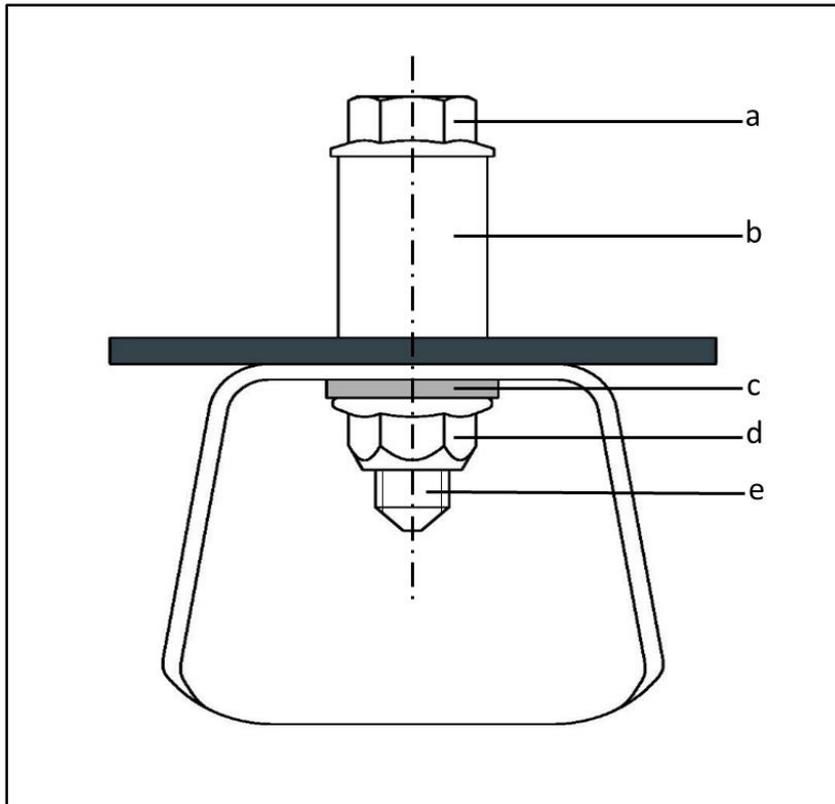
Exemple d'assemblage vissé protégé contre le desserrage (schéma de principe)
